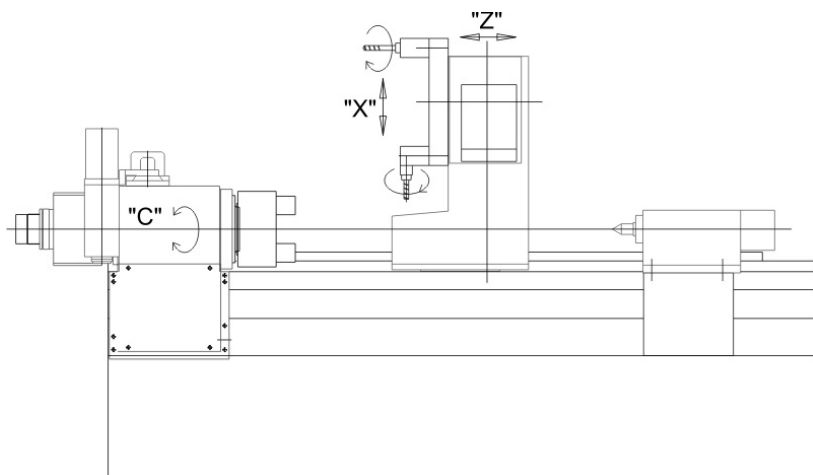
Центр токарный с устройством позиционирования и круговой подачи шпинделя (осью С), револьверной головкой для токарного и приводного инструмента
